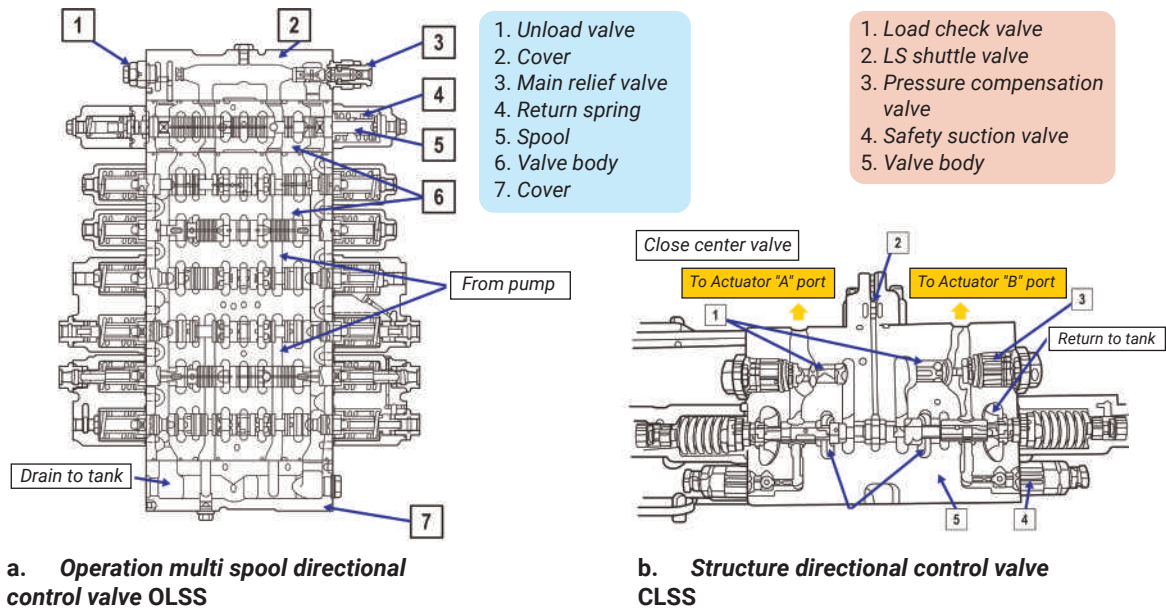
Operation multi spool direction control valve pada open centre (OLSS)
